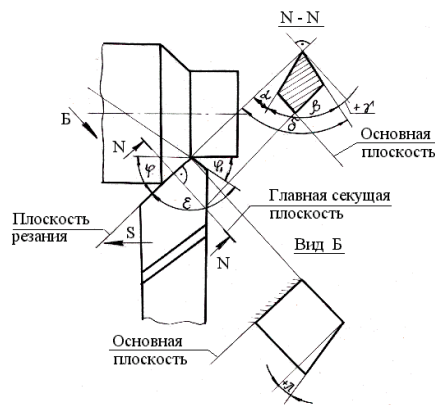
Геометрические параметры режущей части прямого токарного проходного резца
